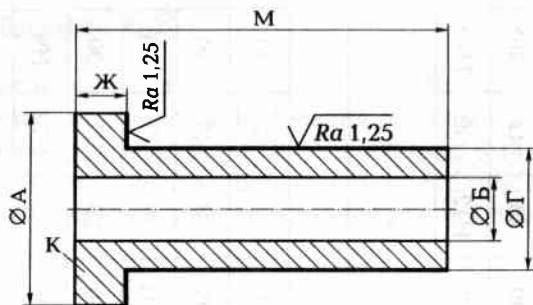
Эскиз заготовки, поступающей на операцию шлифования поверхностей
